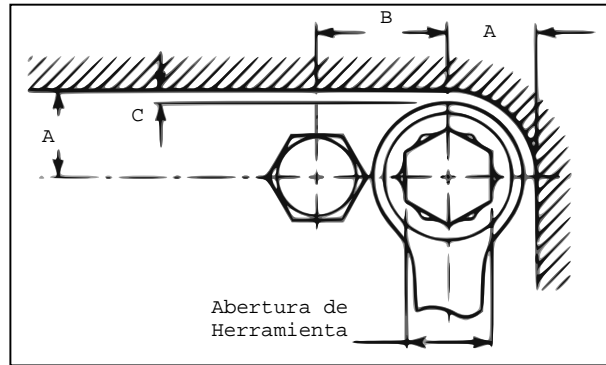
Dimensiones de Herramental de 12 puntos de Agarre
